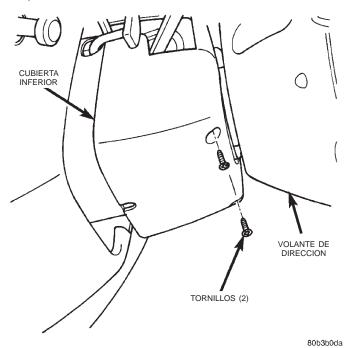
Desmontaje e instalación de cubiertas de la columna de dirección
